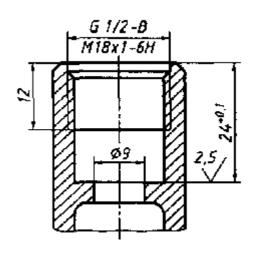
Основные размеры седла клапана и резьб для присоединения вентильных головок
